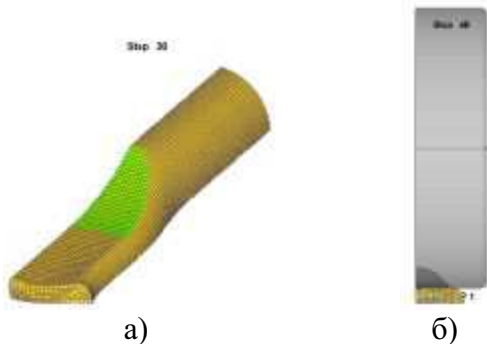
Заготовка и инструмент при вальцовке а) и б)
